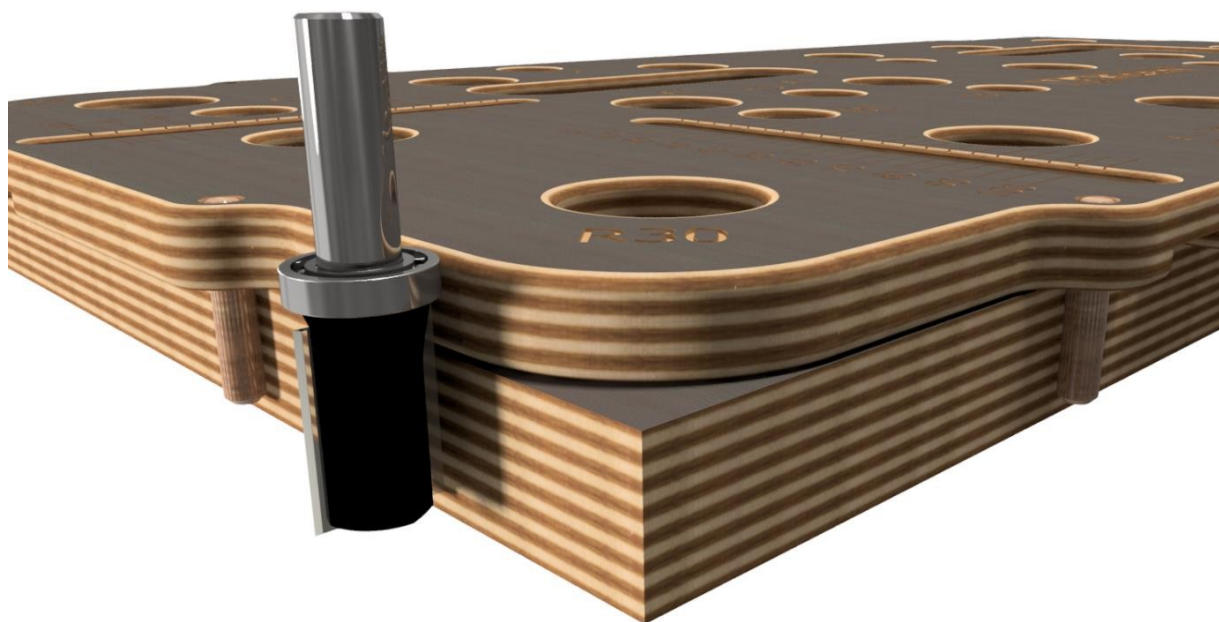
Fresa a filo con cuscinetto a sfere nella parte superiore
